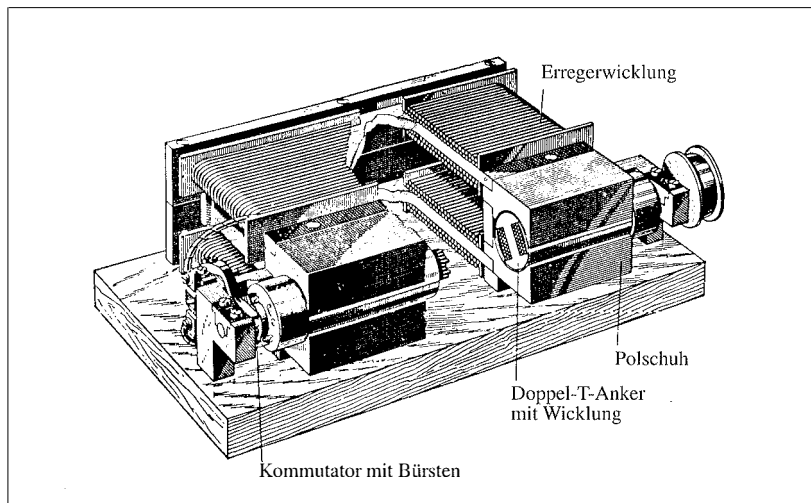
Schnittzeichnung des ersten „Dynamo“, wie Werner Siemens die Maschine nannte
